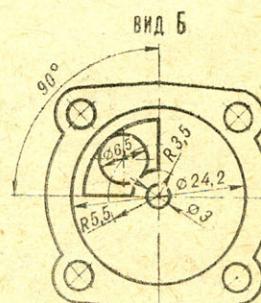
ЗАДНЯЯ КРЫШКА ДВИГАТЕЛЯ.
